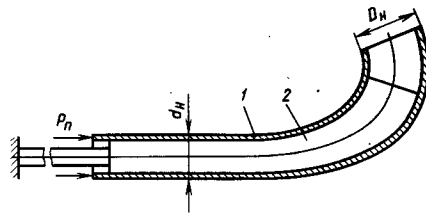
Схема гибки протягиванием через трубу рогообразной оправки: 1 — заготовка; 2 — оправка; d_H — диаметр заготовки; D_H — диаметр детали
